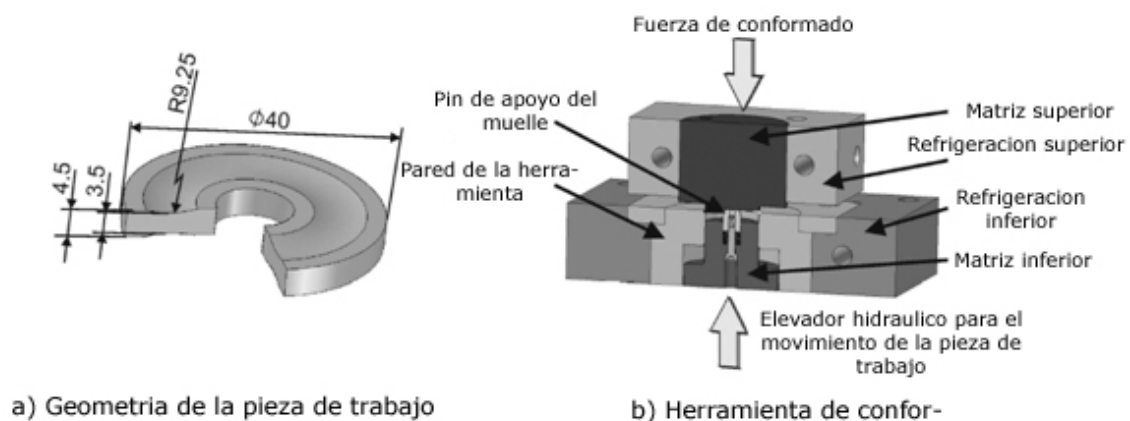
Muestra y herramienta del ensayo sheet bulk metal forming tool. [Wieland, 2012].
